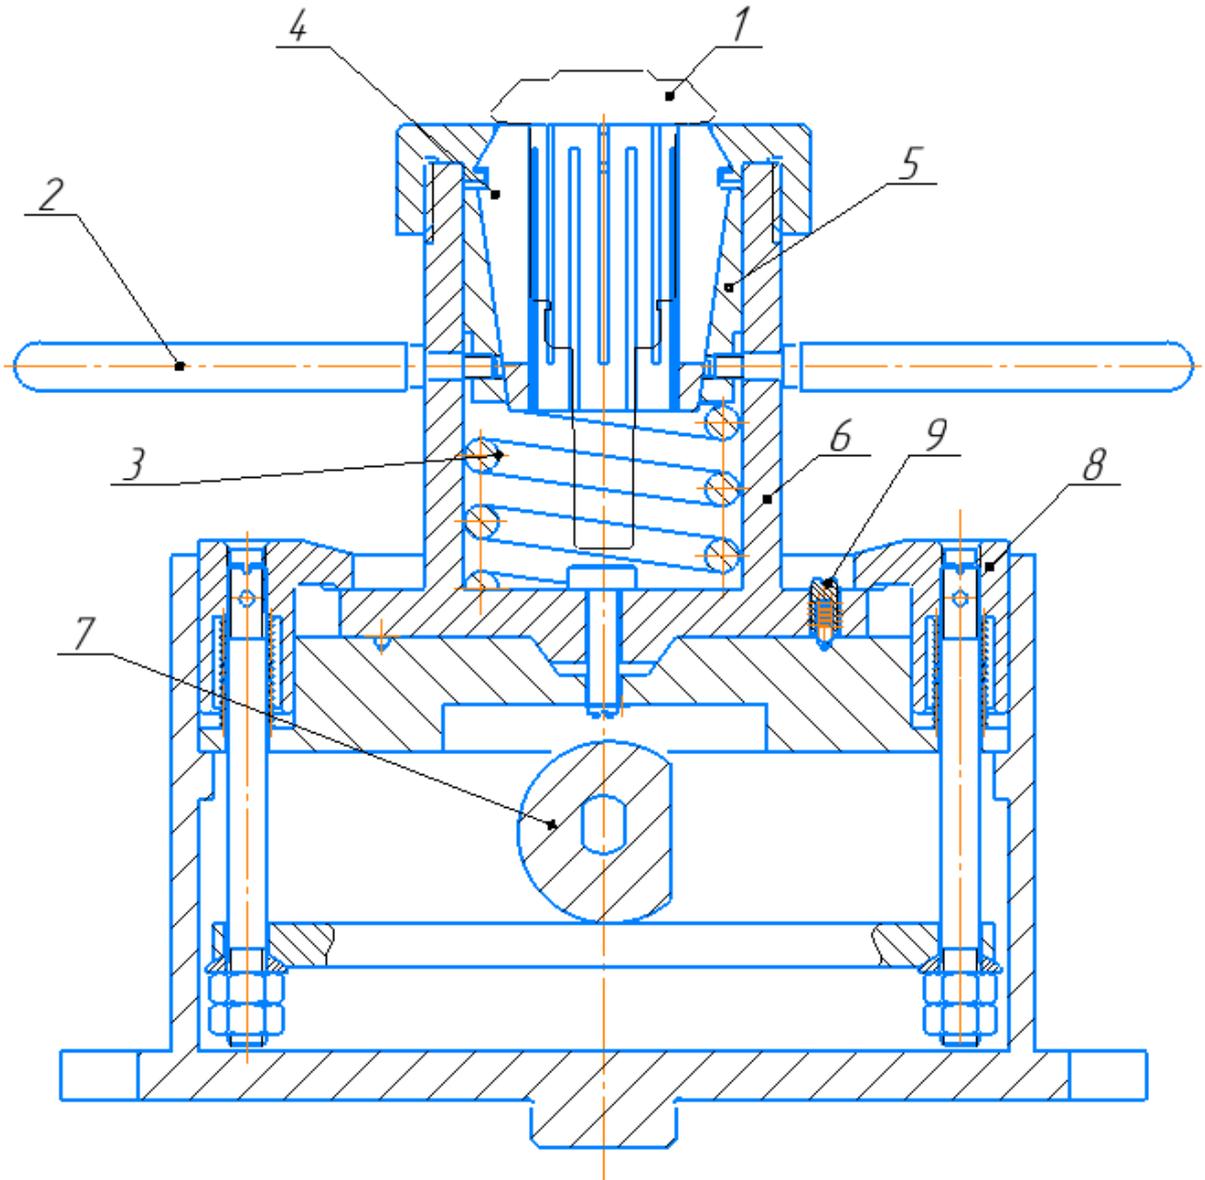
принципиальная схема приспособления. 1 – заготовка, 2 – рычаг, 3 – пружина, 4 – цанговый патрон, 5 – втулка, 6 – корпус, 7 – кулачок, 8 – захваты фиксирующие, 9 – винт-фиксатор.
